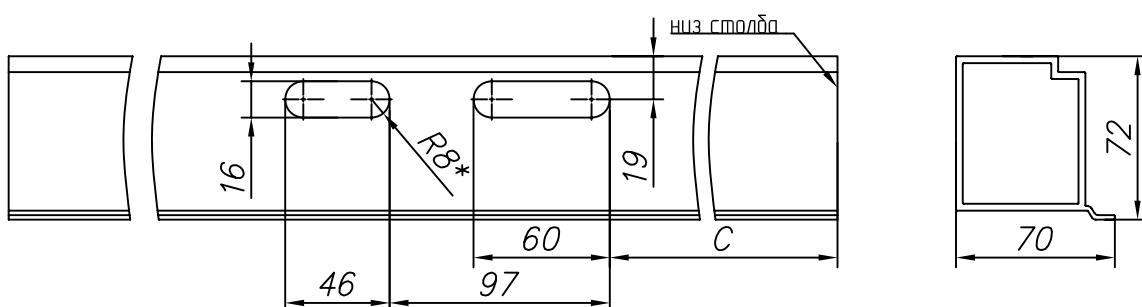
Изготовление столба притвора с пазом для ответной пластины замка для калитки с левым открыванием
